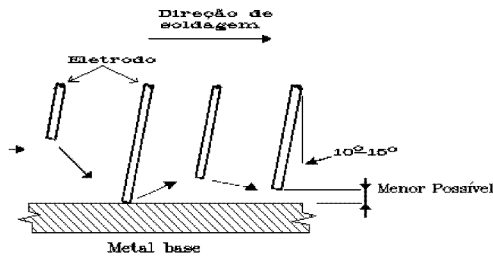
Movimento a ser realizado pelo soldador com o eletrodo para iniciar a soldagem.
